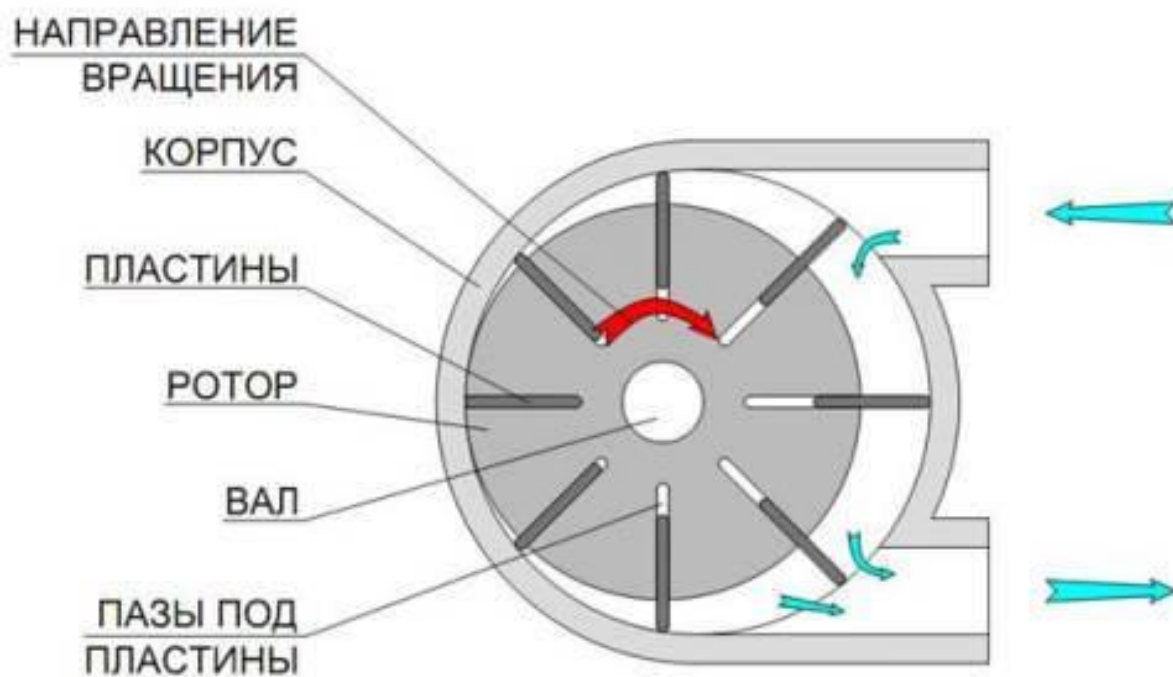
Чертеж роторно-пластинчатого компрессора.
